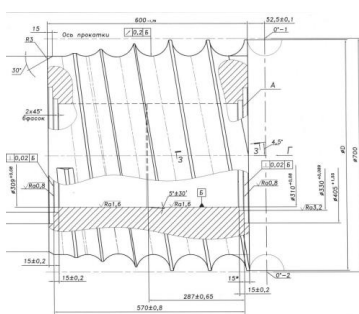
Прокатный валок с двухзаходной калибровкой для прокатки шаров диаметром 100 мм
